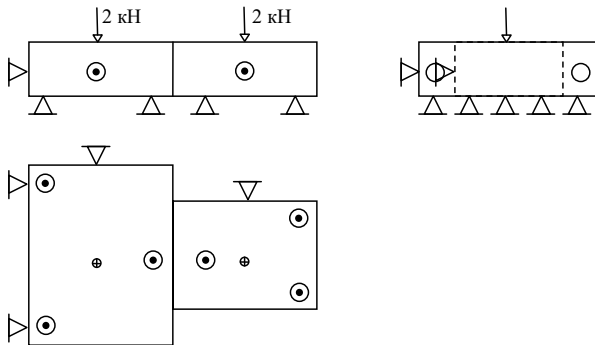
Принципиальная схема приспособления для сборки изделия
